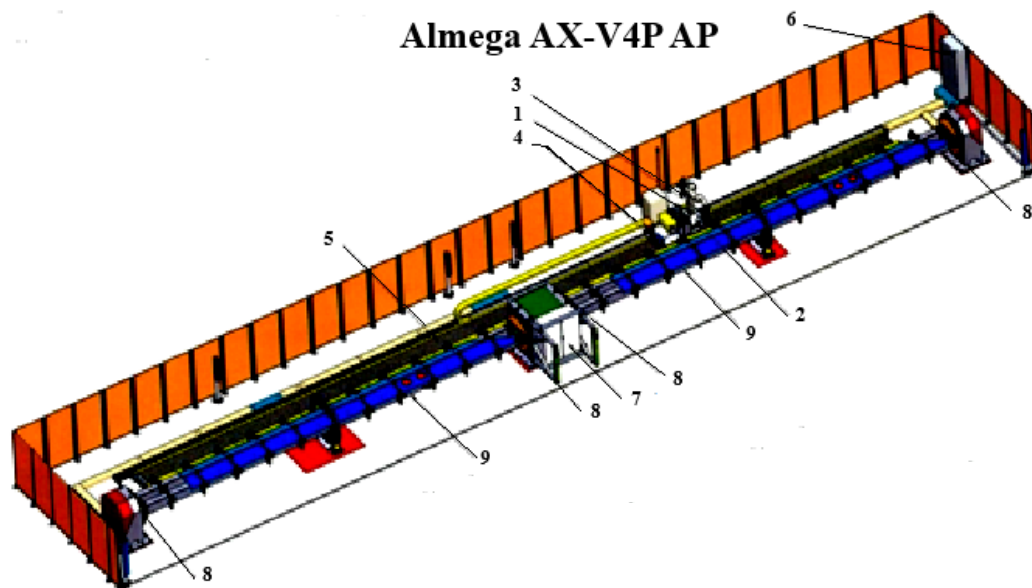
Общая компоновка линии сварки узлов шасси большегрузных автомобилей (сборка лонжеронов):
